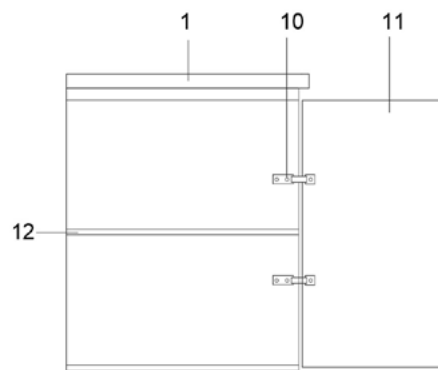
Detalle constructivo mueble de cocina HDPE reciclado
